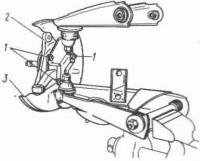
Conjunto suspensión de la rueda izquierda afianzado en el banco de ajustador para el despiece:
